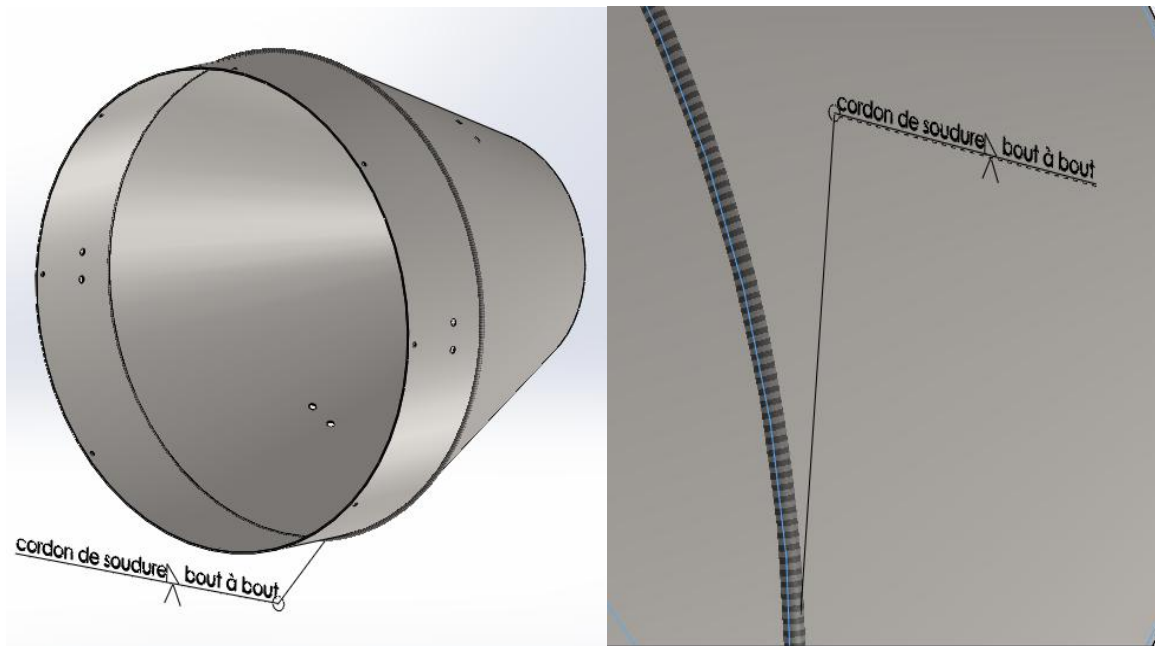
Assemblage des deux parties de la cuve avec soudage bout à bout.
